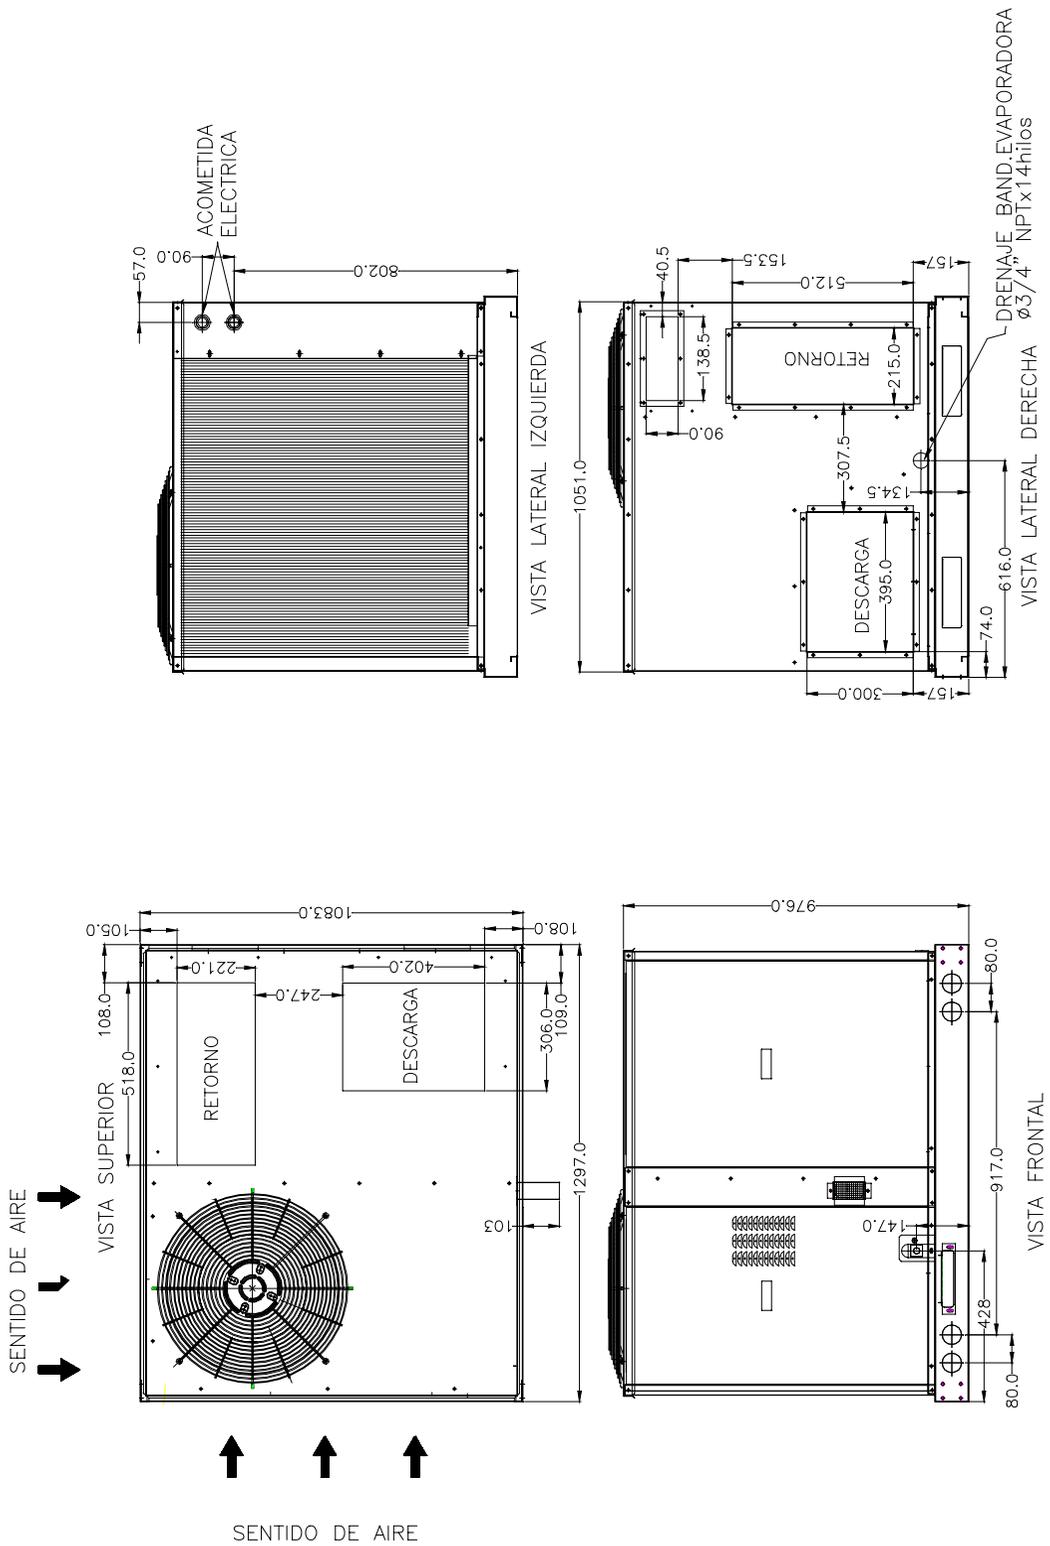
Dimensiones de la Unidad – 582N 036/057
